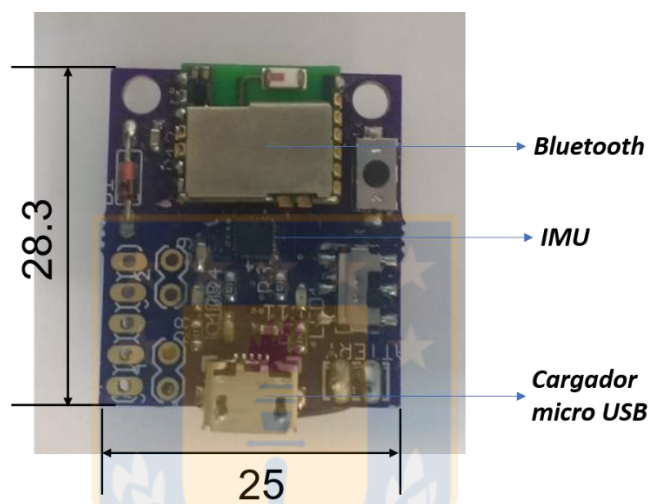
Placa PCB de la unidad de medición confeccionada con cotas en milímetros.
